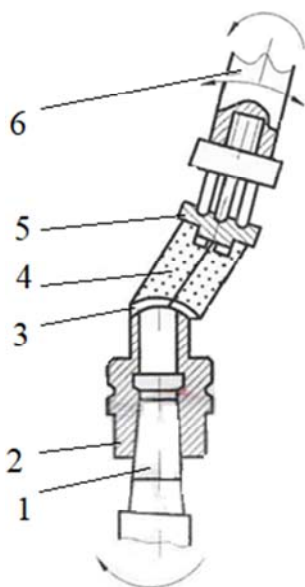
Схема полирования выпуклой поверхности заготовки линзы:
